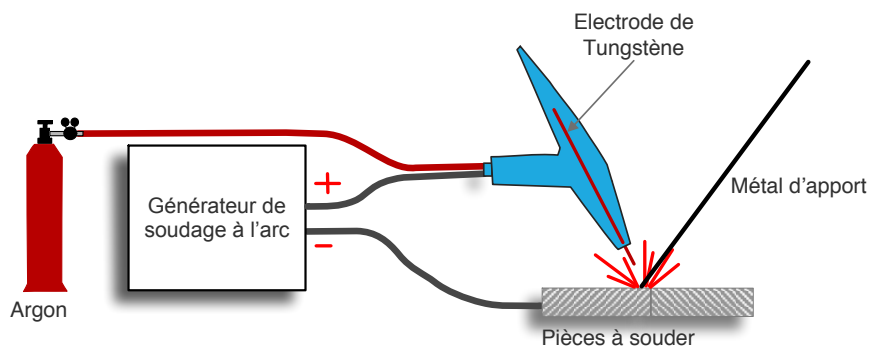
Schéma de principe du soudage TIG
